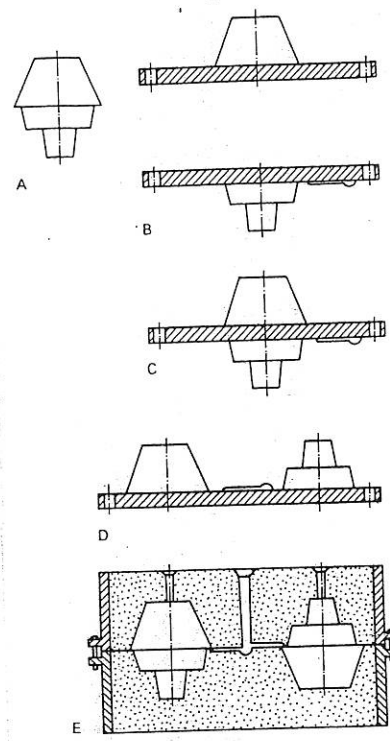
Diversos modelos de placa: A, pieza; B, placas simples; C, placa de doble cara; D, placa reversible; E, molde.
